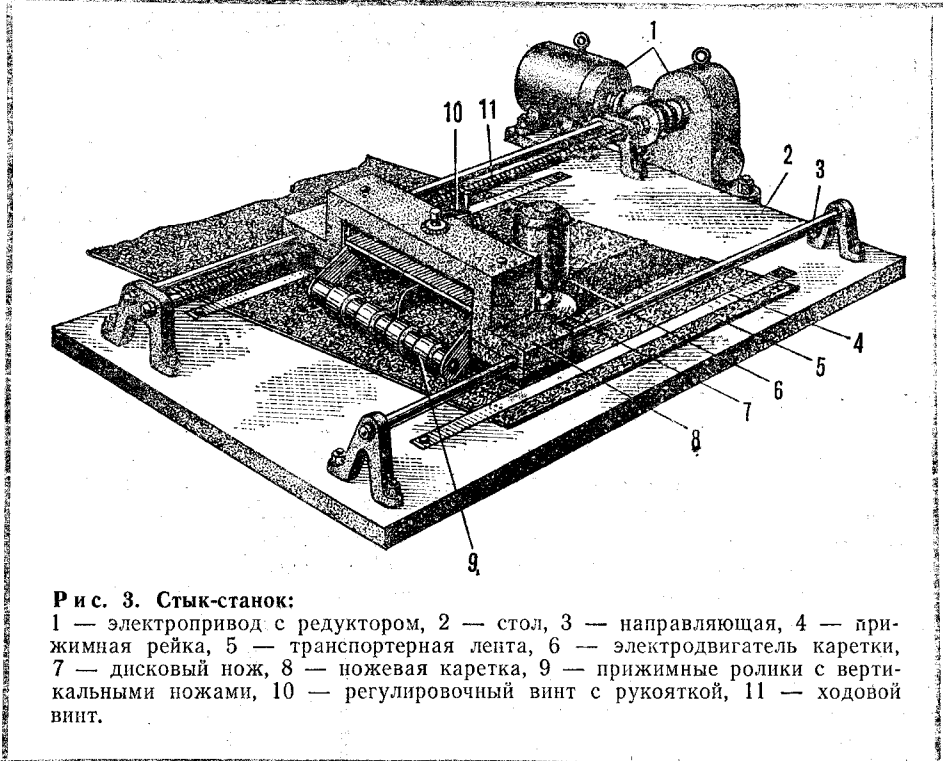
Стык-станок: 1 — электропривод с редуктором, 2 — стол, 3 — направляющая, 4 — прижимная рейка, 5 — транспортерная лента, 6 — электродвигатель каретки, 7 — дисковый нож, 8 — ножевая каретка, 9 — прижимные ролики с вертикальными ножами, 10 — регулировочный винт с рукояткой, 11 — ходовой винт.
